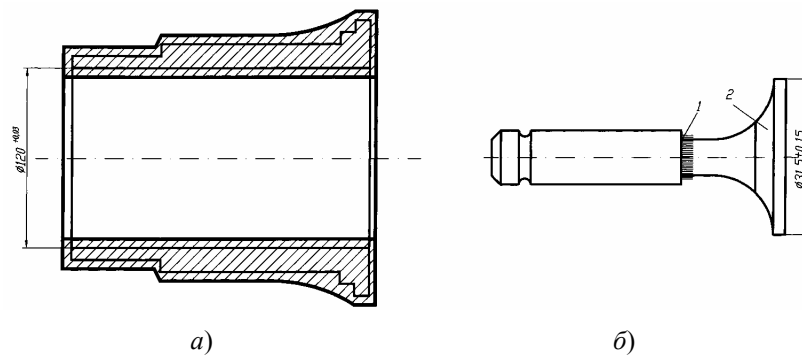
Заготовки для гильзы цилиндра (а) и для клапана сварной конструкции (б):
